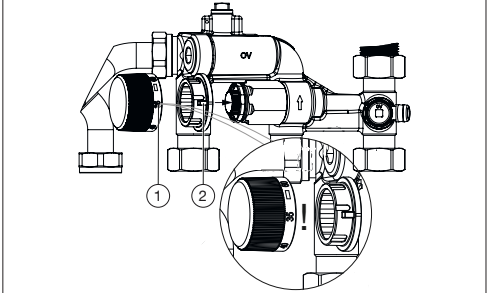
Montage de la douille graduée et de la poignée manuelle
